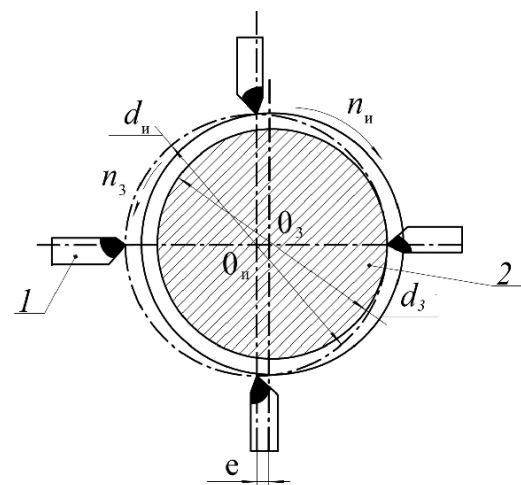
Схема скоростного фрезерования резьбы при внутреннем касании инструментальной головки 1 (четыре резца) с обрабатываемой поверхностью заготовки 2
